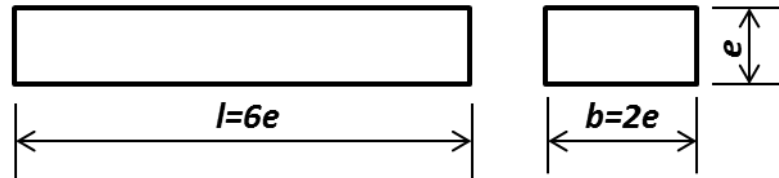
Geometría y dimensiones de la probeta para el ensayo de ILSS
